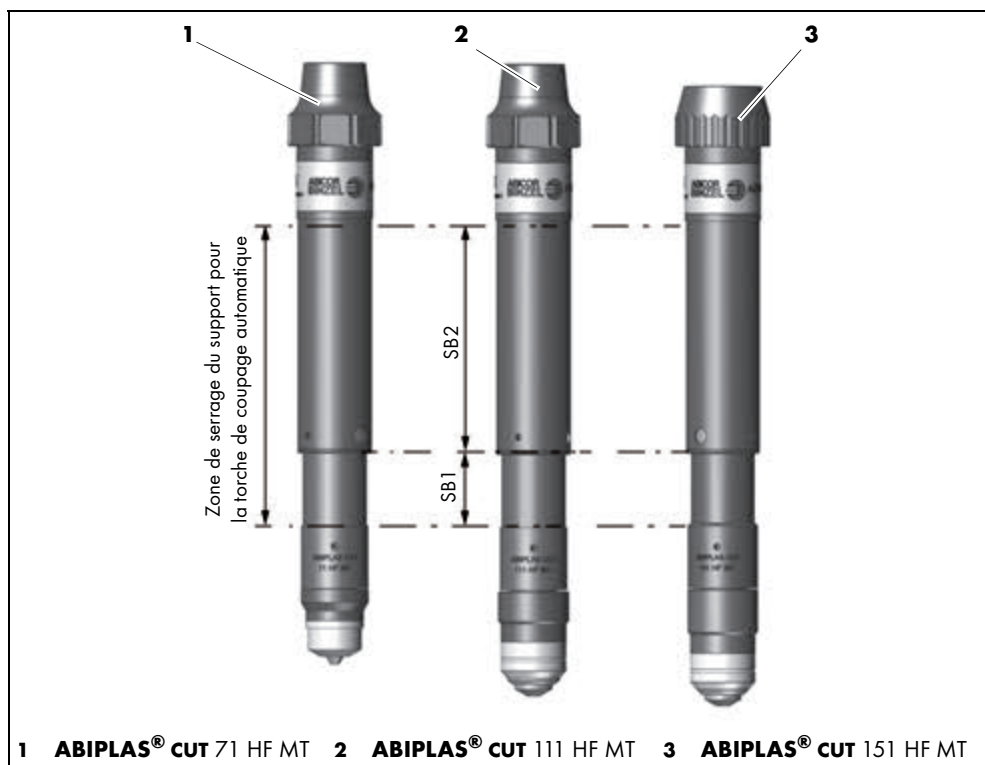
Vue d'ensemble d'ABIPLAS® CUT 111 HF MT
